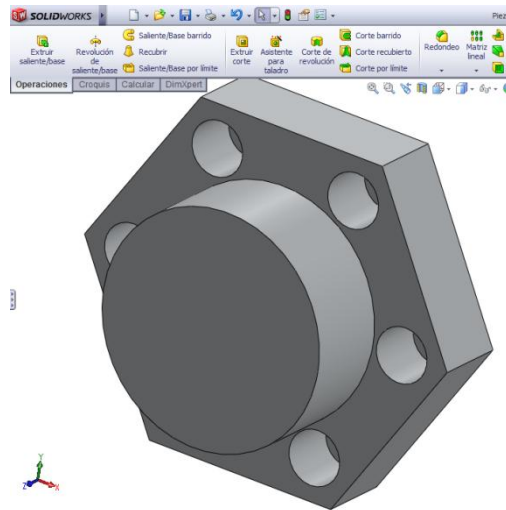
Diseño de la pieza de torneado y fresado en SolidWorks.
